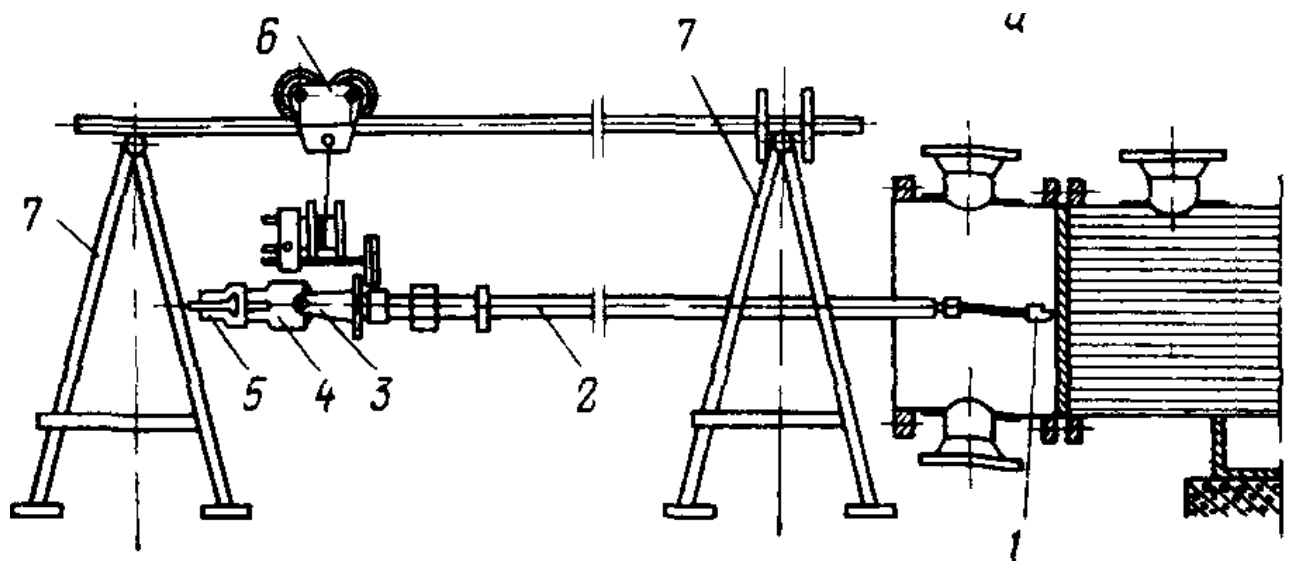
Приспособление для механической чистки котла-утилизатора
